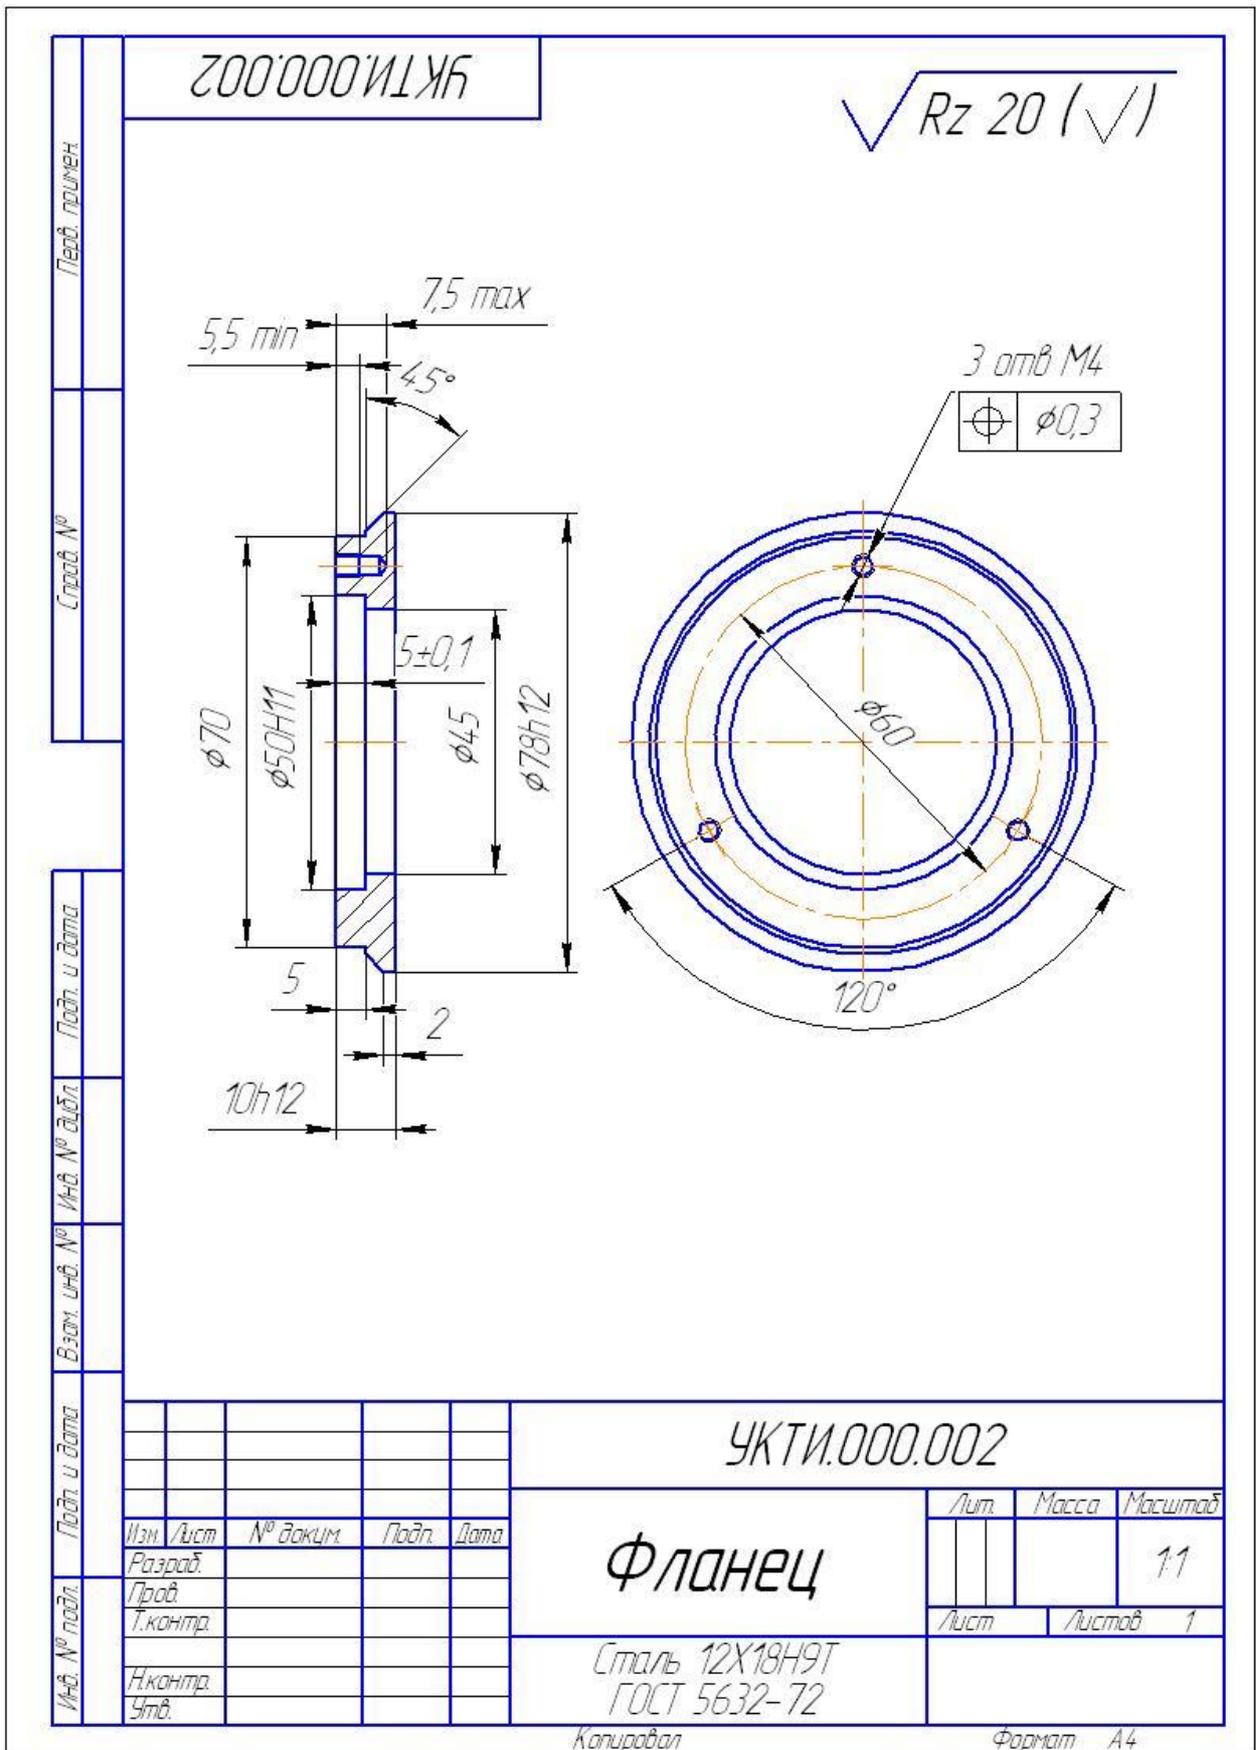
Чертеж детали УКТИ.000.002 Фланец
